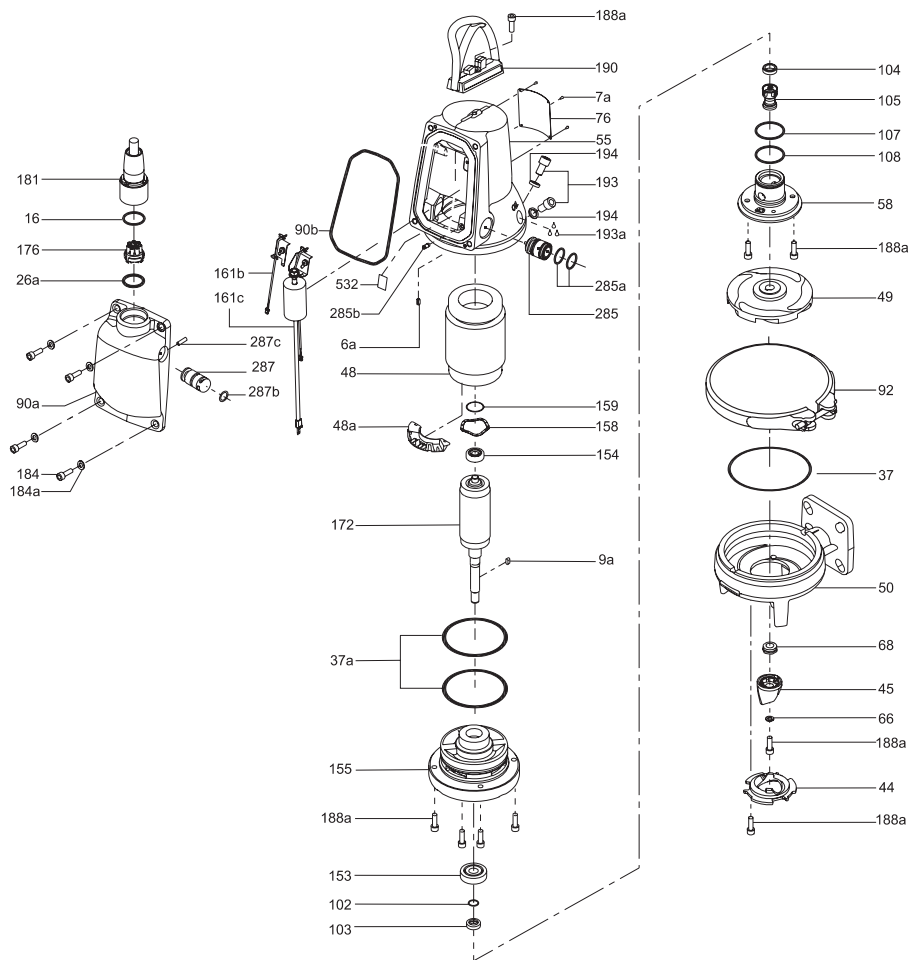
Деталировка насоса SEG AUTOADAPT (0,9-1,5 кВт)
